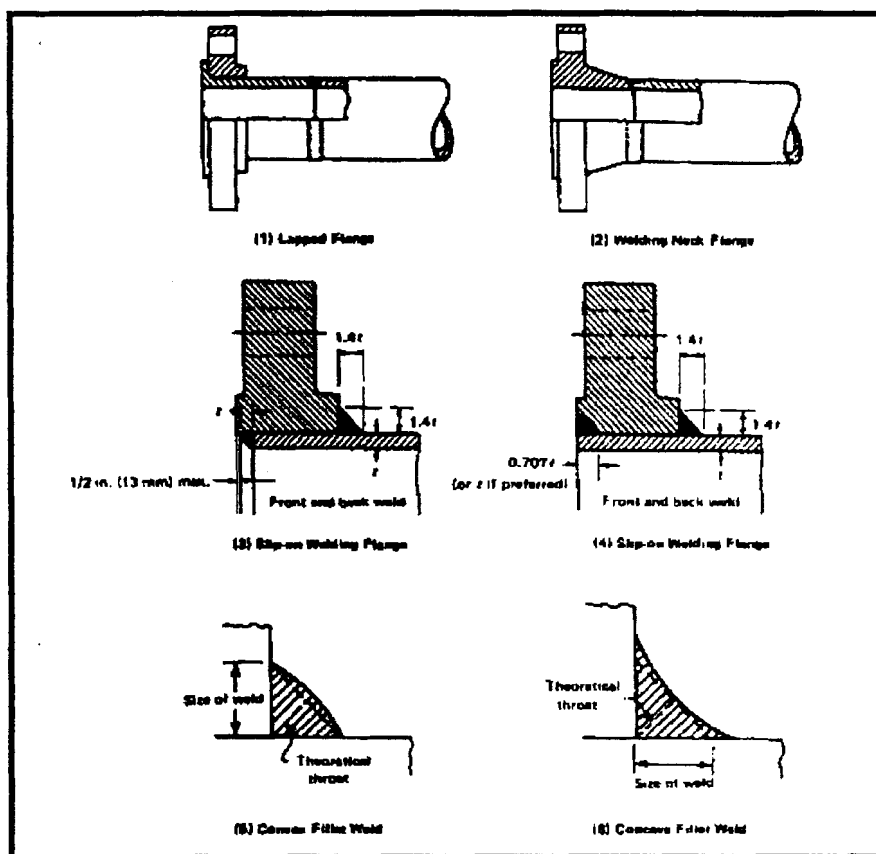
RECOMENDACIÓN EN LA UNIÓN DE LAS BRIDAS A LA TUBERÍA
